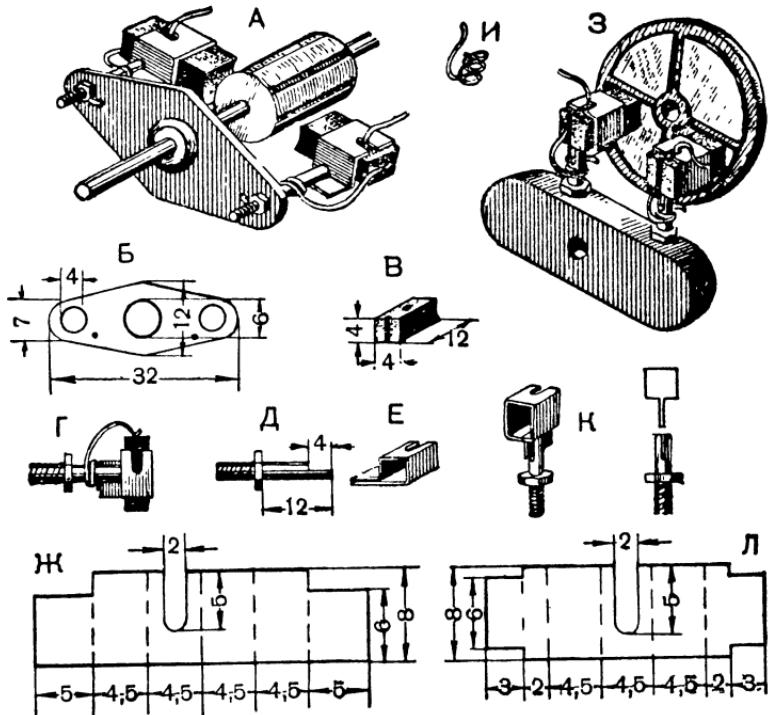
Конструкции угольных щеток. Щетки для цилиндрического коллектора: А — общий вид; Б — пластина щеткодержателя; В — угольная щетка; Г — крепление прижимной пружины; Д — укороченная ножка от вилки; Е — обойма; Ж — развертка обоймы. Щетки для дискового коллектора: З — общий вид; И — прижимная пружина; К — обойма и ее крепление в ножке от вилки; Л — развертка обоймы.
